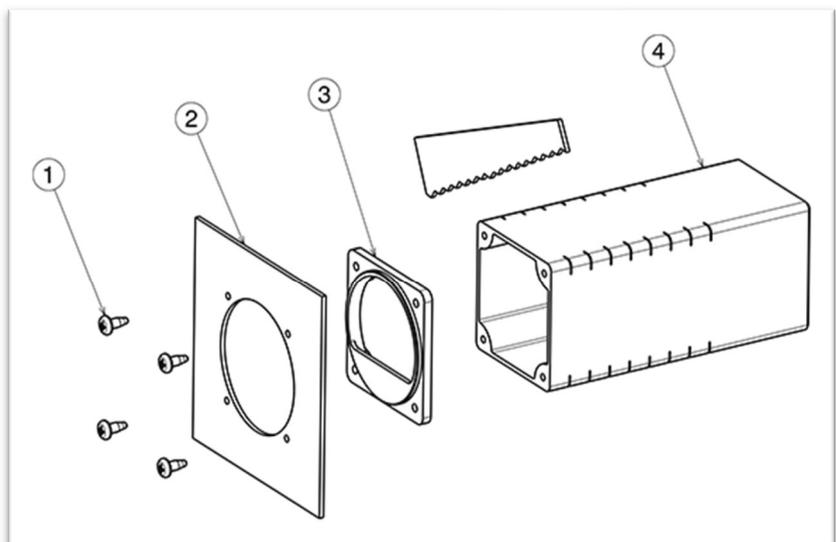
Technische Zeichnung Explosionszeichnung Anordnung I-Brett Ablage
